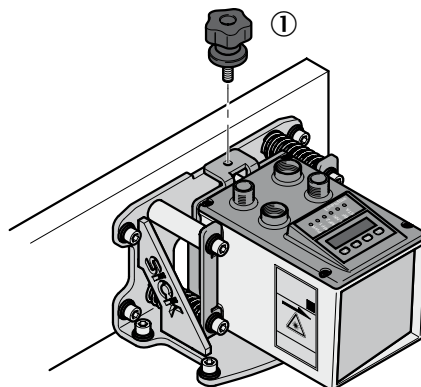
Entfernungs-Messgerät mit Rändelschraube befestigen
